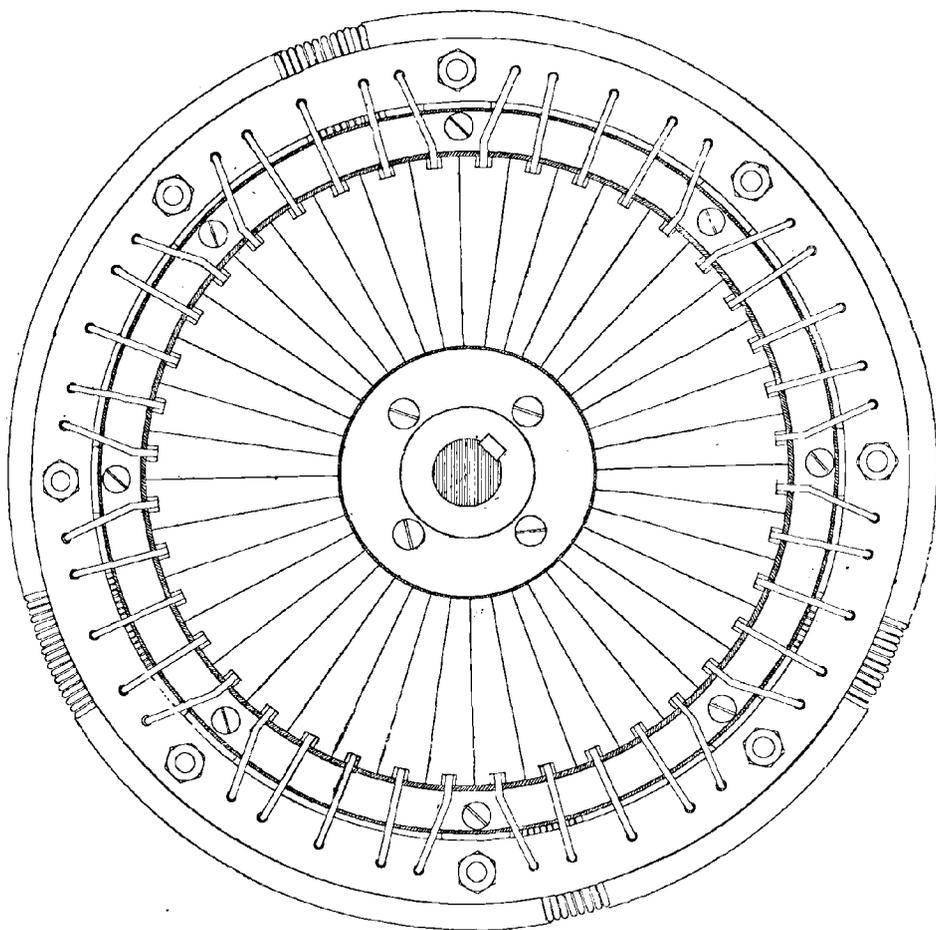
Moteur Meynier et Legros (Vue du collecteur).
